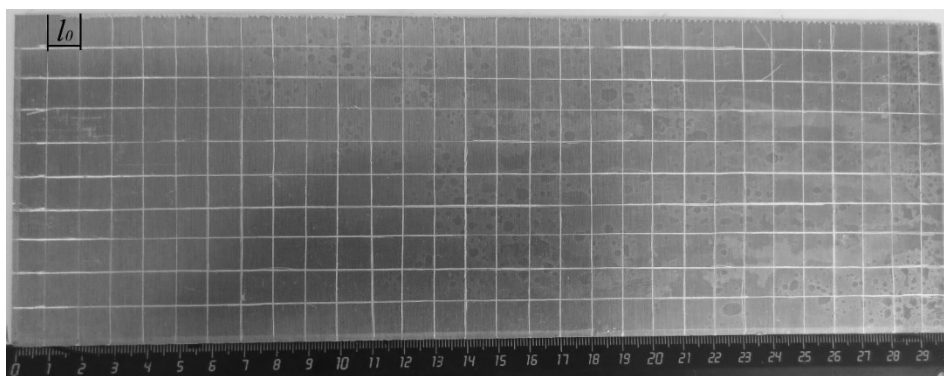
Основная пластина из АМгб с координатной сеткой до сварки взрывом
